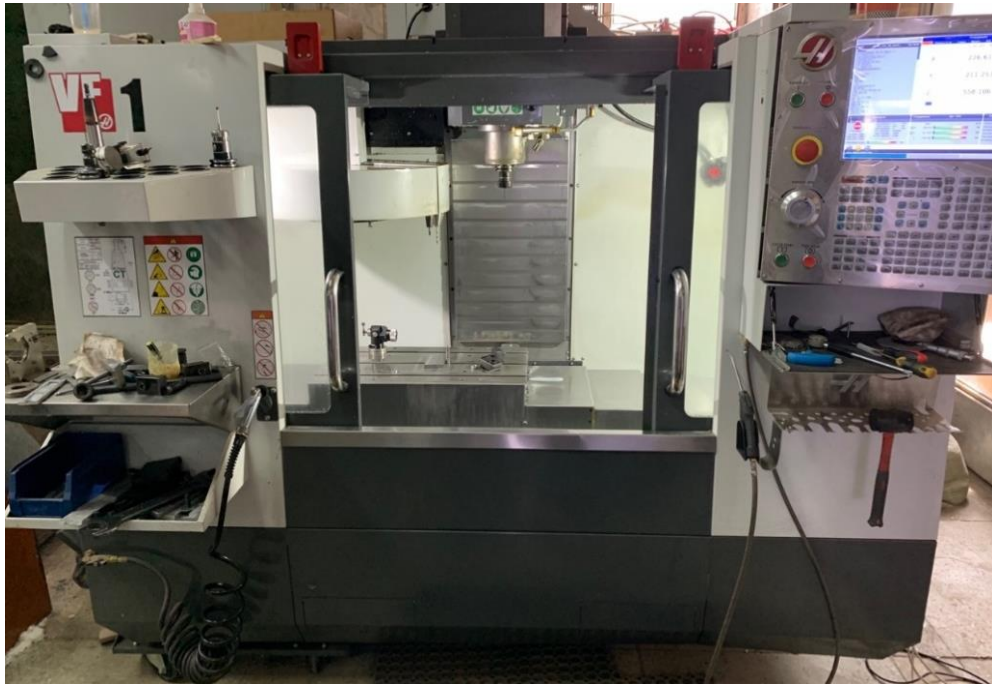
Вертикально-фрезерный обрабатывающий центр с ЧПУ Haas VF-1
